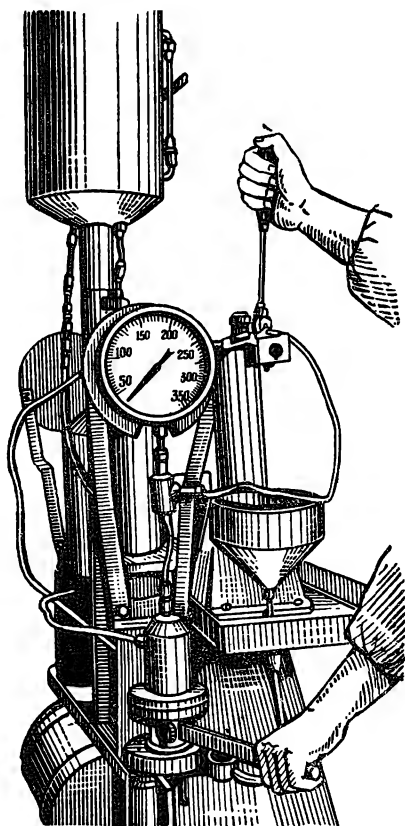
Стенд для регулировки давления впрыска топлива форсунками
